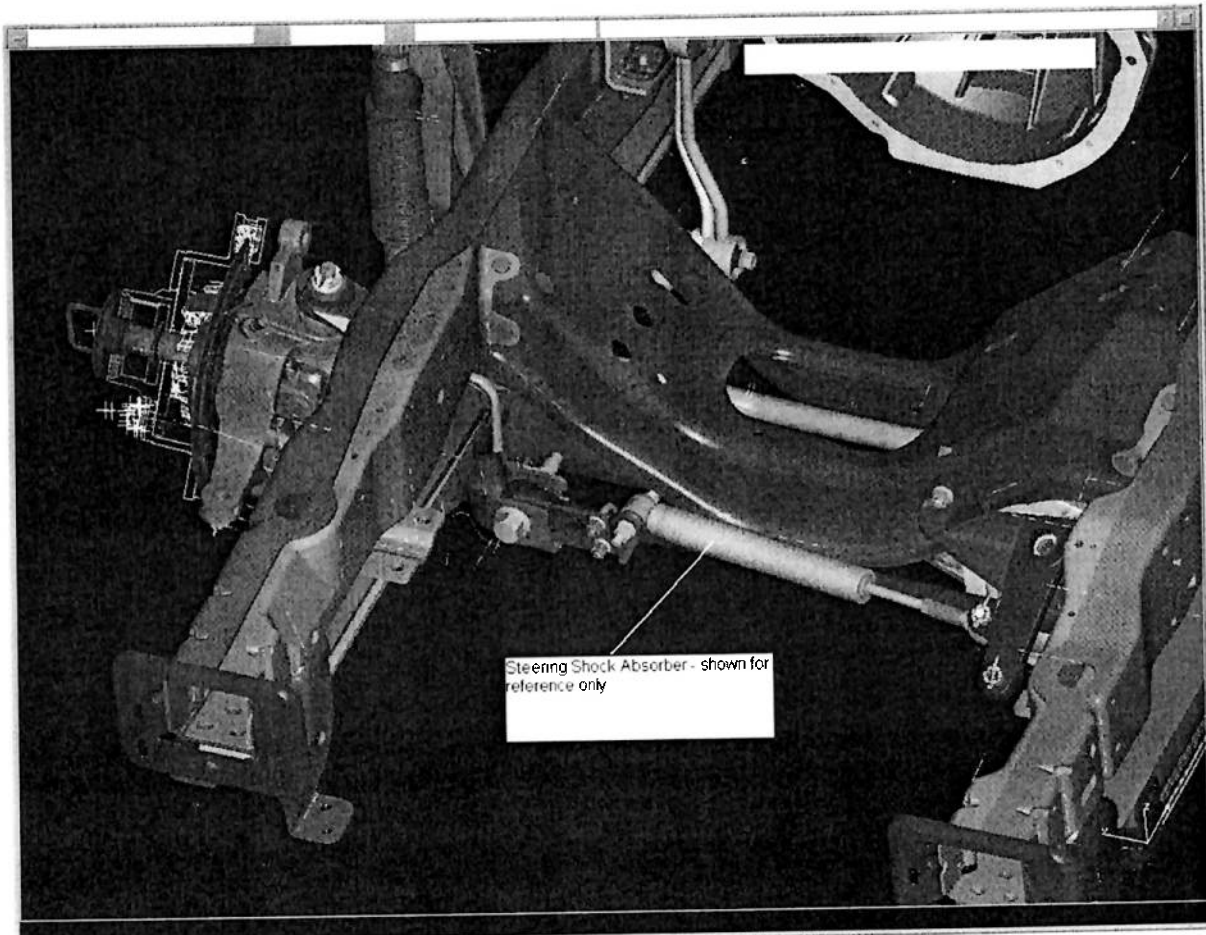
Chassi PU 121"wb 4x4 – Conjunto Dianteiro
